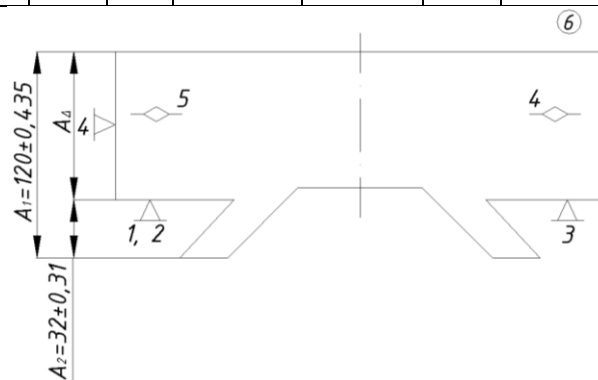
Схема базування заготовки при обробленні пов.6
